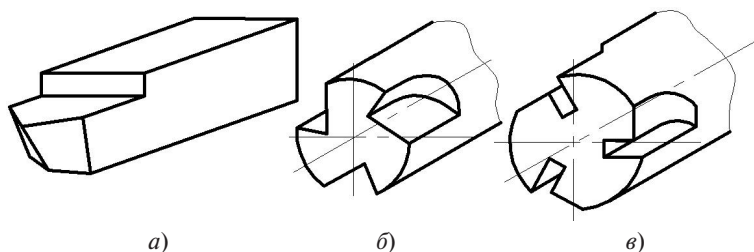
Формы пазов в корпусах инструмента под режущие пластины твердого сплава: *а*) открытая, *б*) полуоткрытая; *в*) закрытая
